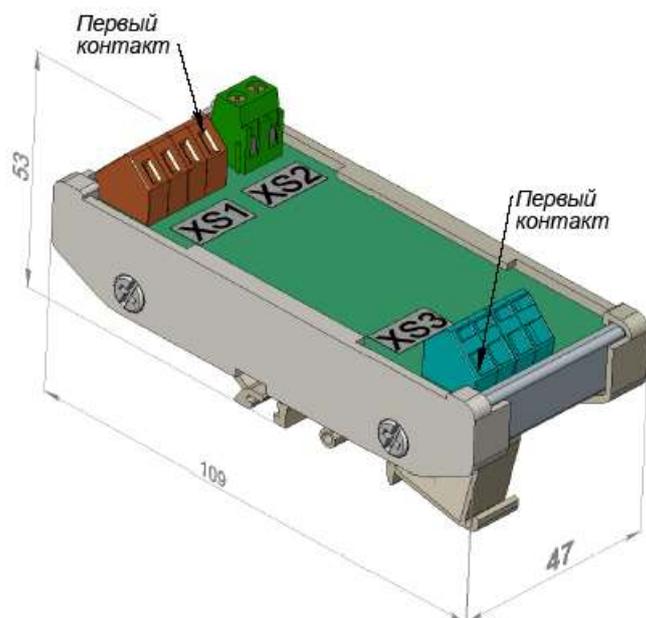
Внешний вид и габаритные размеры барьера ТСС Ex2А
